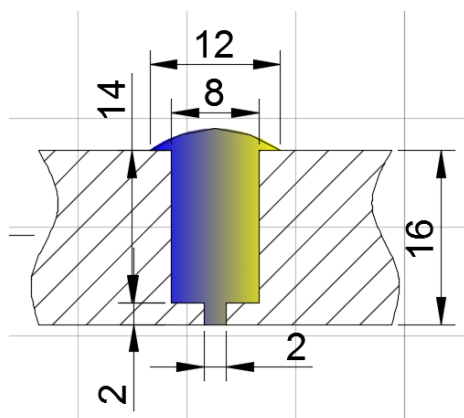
Сечение сварного стыка труб  $\varnothing 1220$  мм и толщиной стенки 16 мм, при использовании сварки с импульсным питанием
